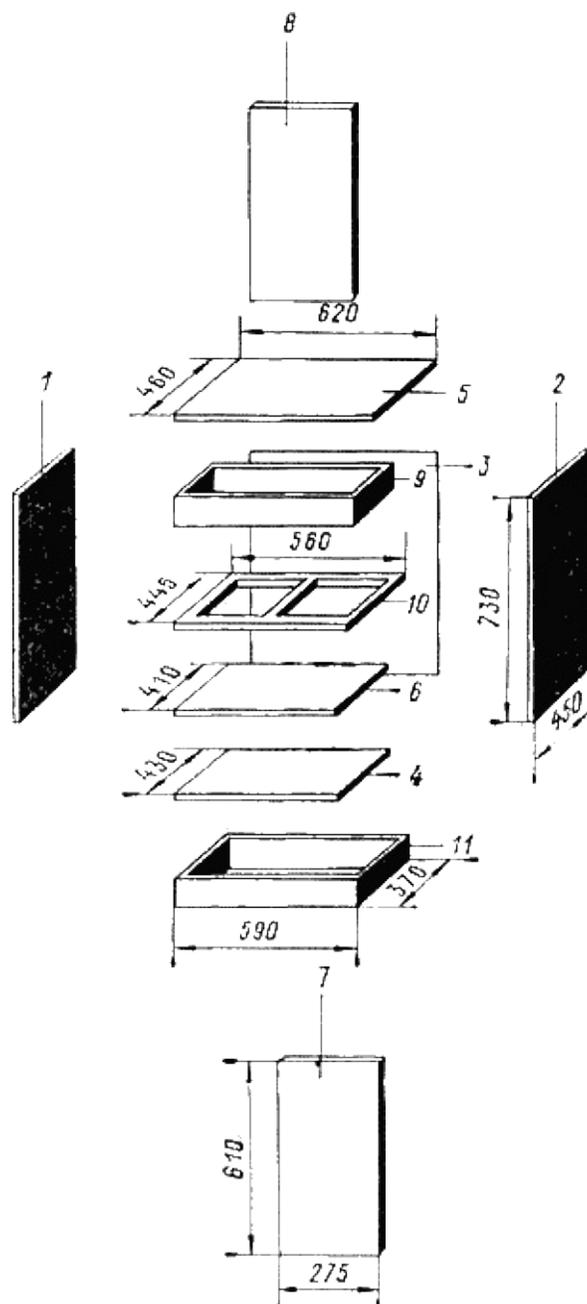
Основные детали разделочного стола-шкафа: 1 и 2 — боковые стенки; 3 — задняя стенка; 4 — днище (нижний полк); 5 — крышка; 6 — полка; 7 и 8 — дверки; 9 — ящик; 10 — подъящичная рамка; 11 — цоколь
